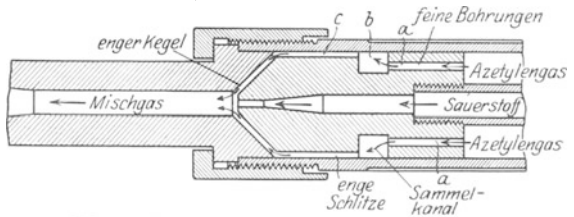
Schweißbrenner mit Rückschlagsicherung.
